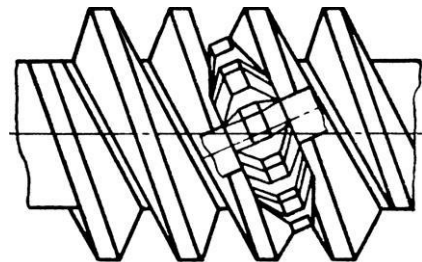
Нарізання черв'яків дисковою фрезою
